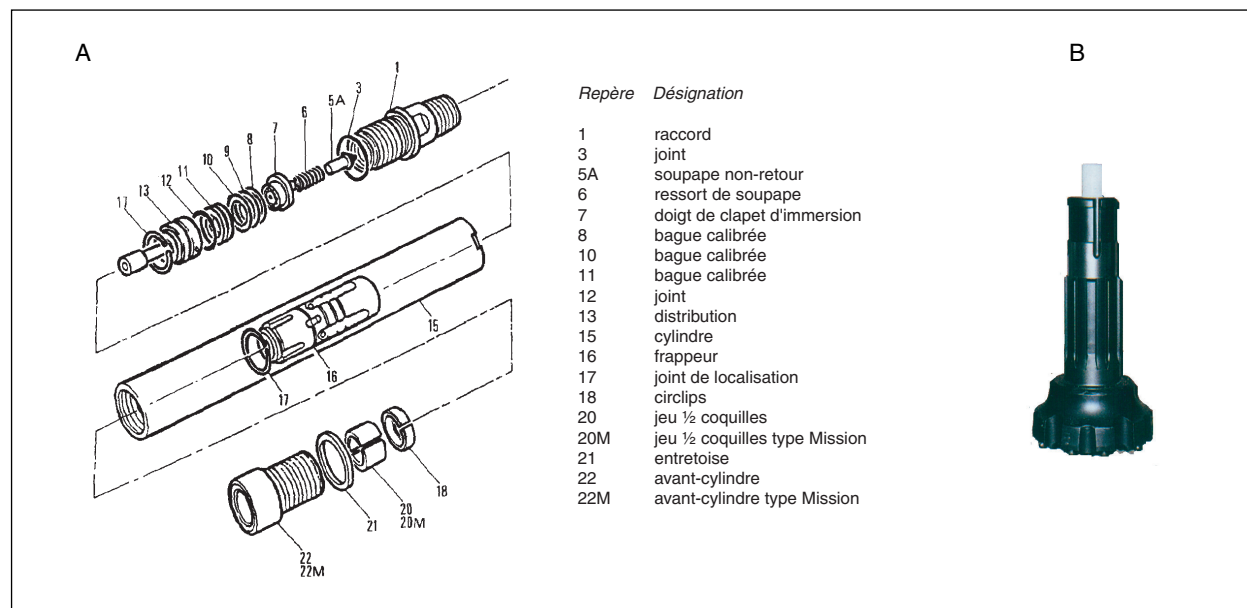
Marteau fond de trou. A, liste de pièces détachées du MFT. B, taillant
